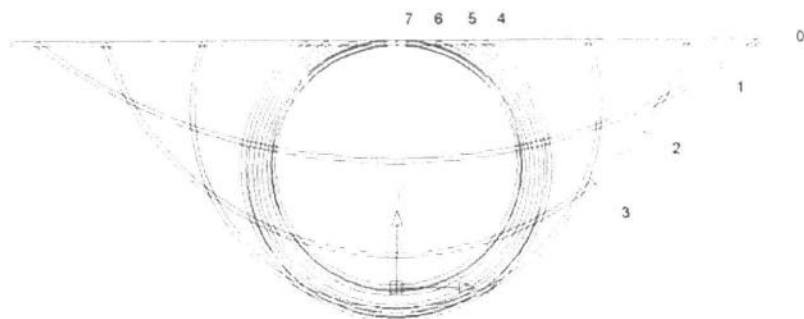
Профиль заготовки при формовке в несколько проходов.
